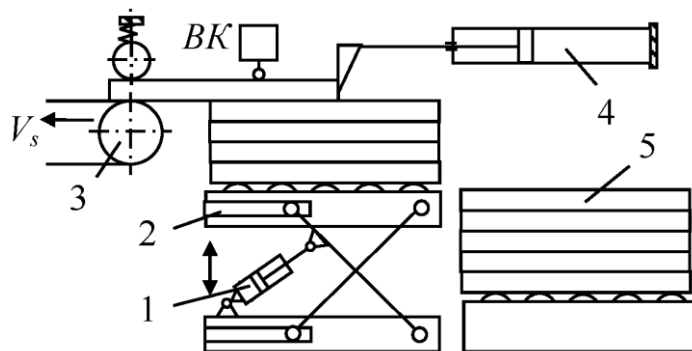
Завантажувально-розвантажувальний пристрій для щитових деталей
